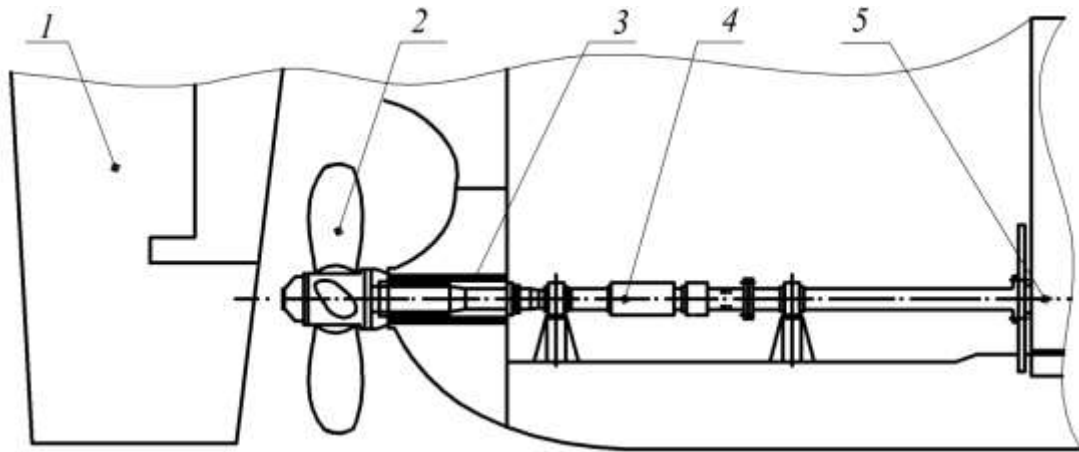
Типовой винто-рулевой комплекс судна транспортного судна: 1 – перо руля; 2 – гребной винт; 3 – дейдвудная труба; 4 – валопровод; 5 – главный двигатель
